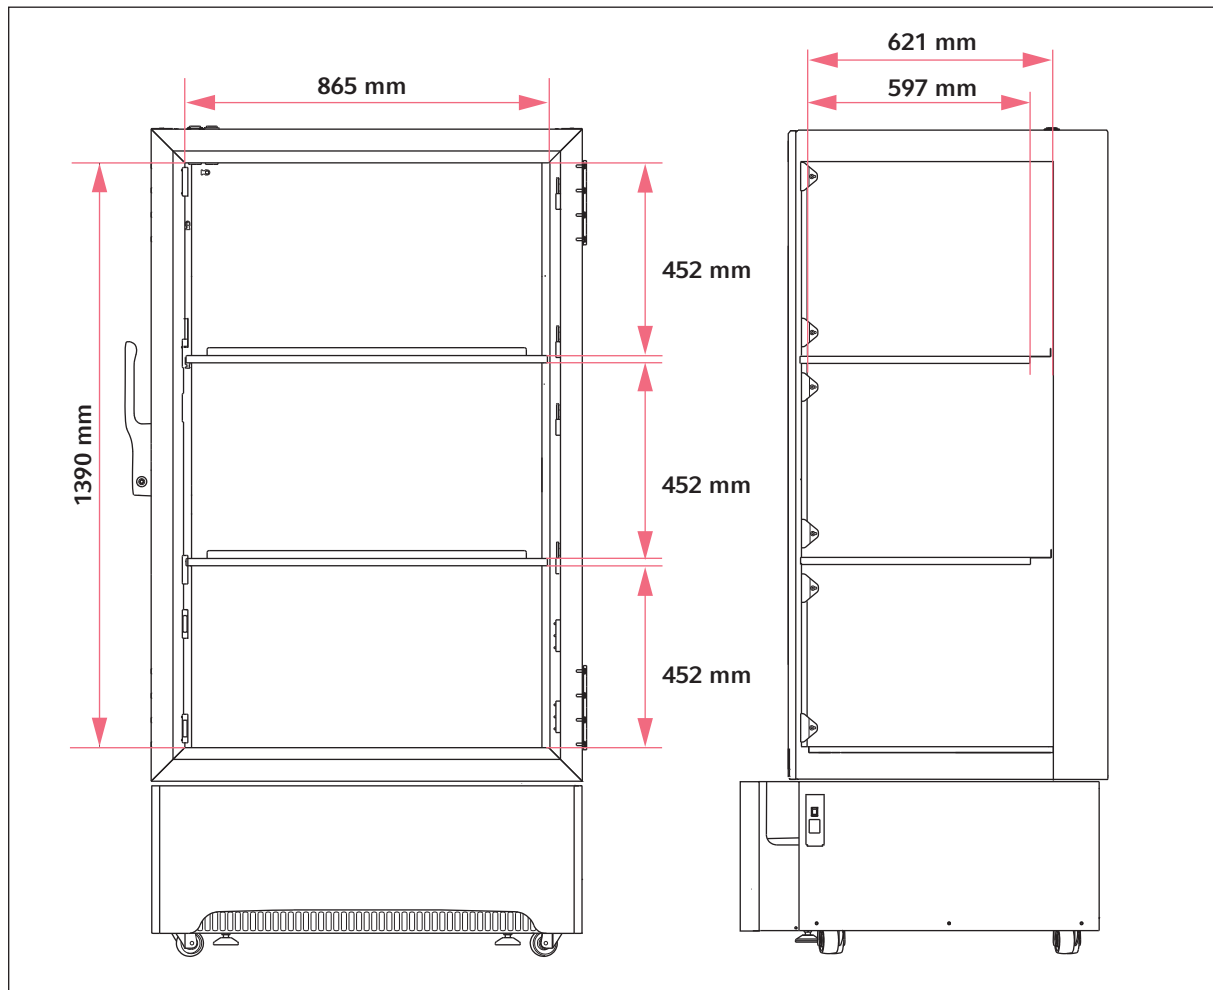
Innenmaße für Geräte mit 3 Innenfächern
